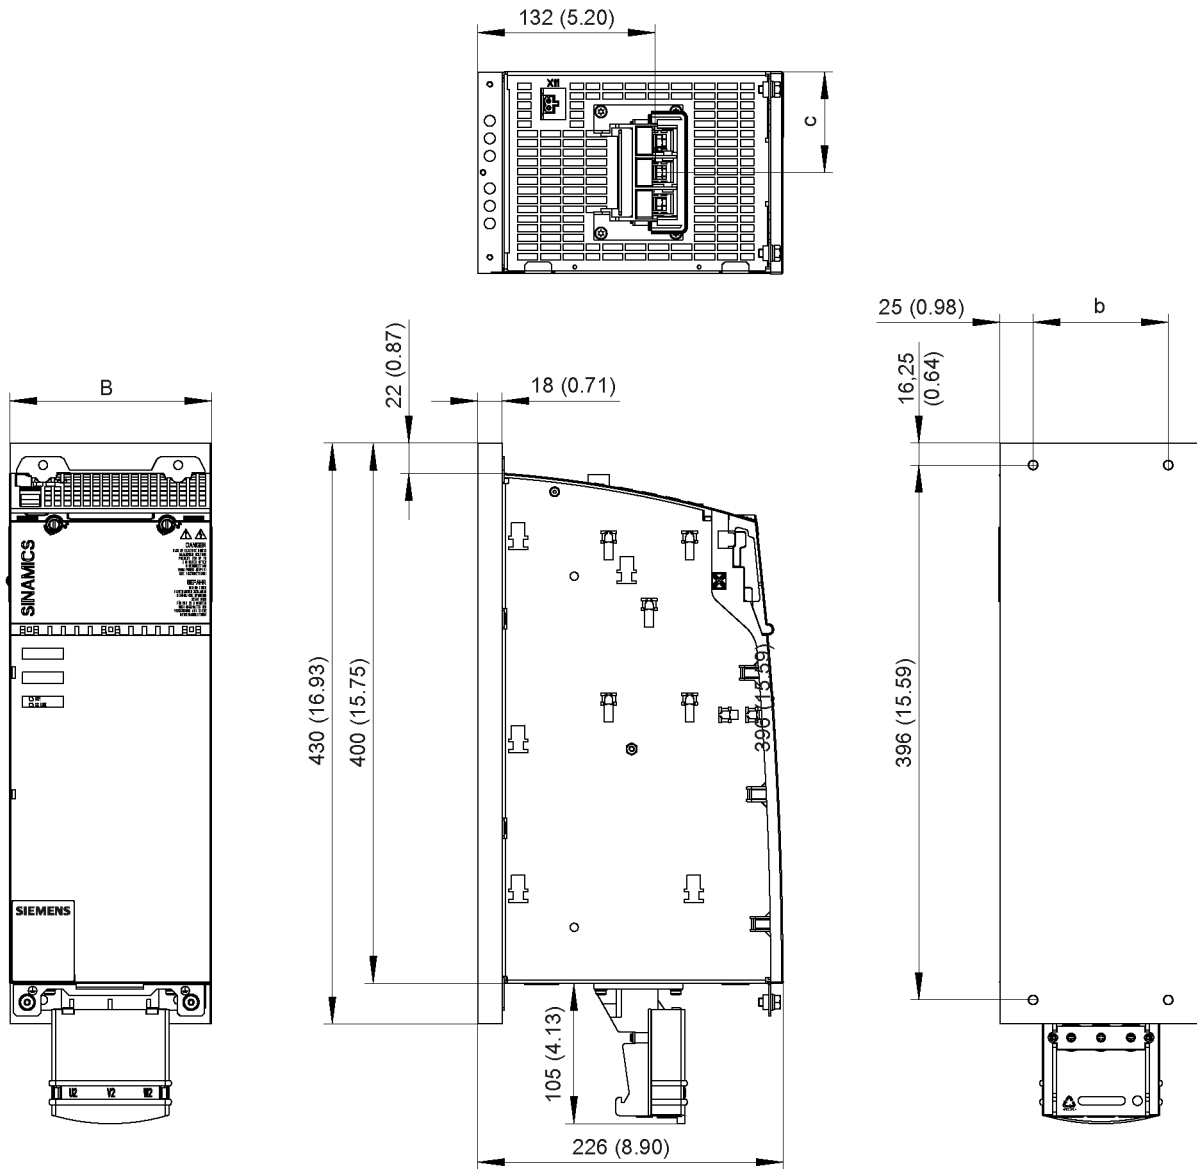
Croquis acotado de Motor Modules Booksize de 45 A, 60 A y 85 A con Cold Plate, todas las medidas en mm y (pulgadas); ejemplo de Motor Module de 45 A
